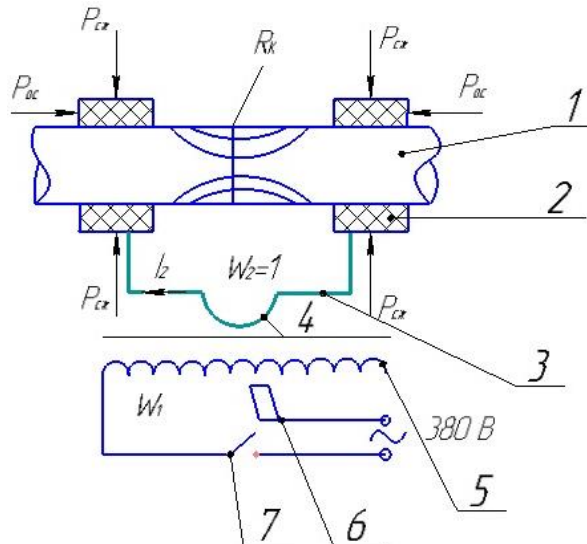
Схема стыковой контактной сварки:
